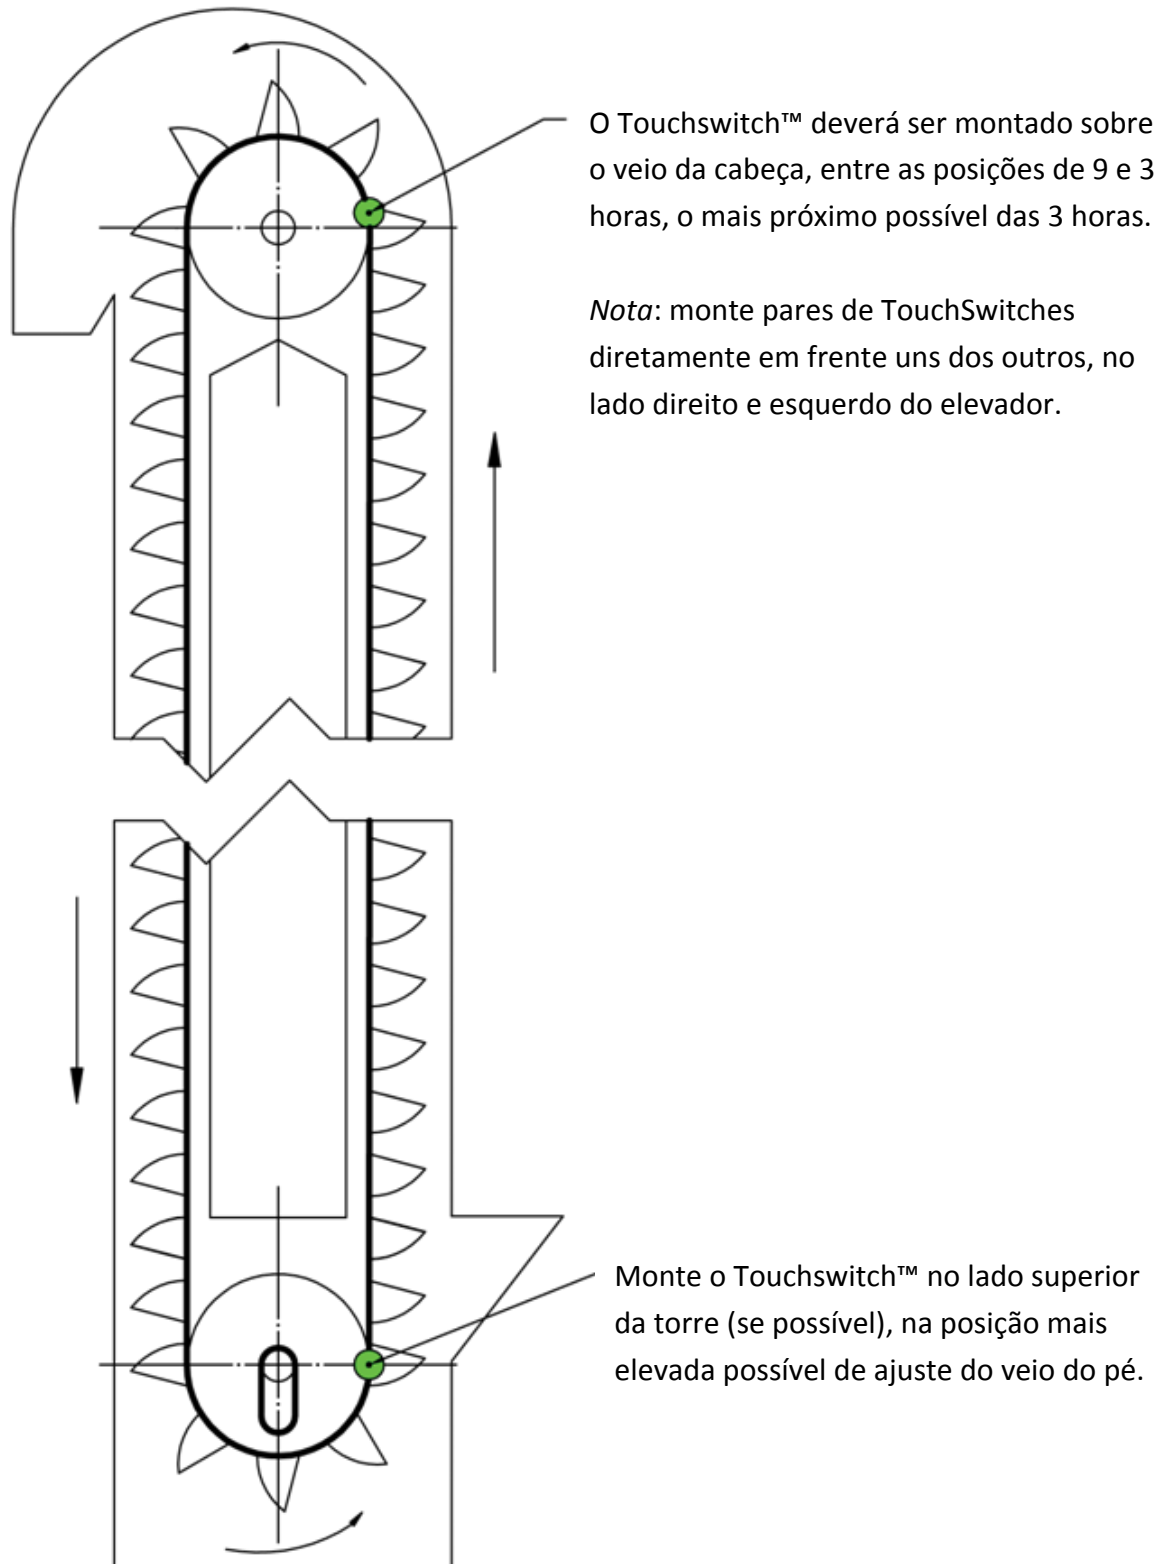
Posições de montagem do Touchswitch – Torre do elevador
